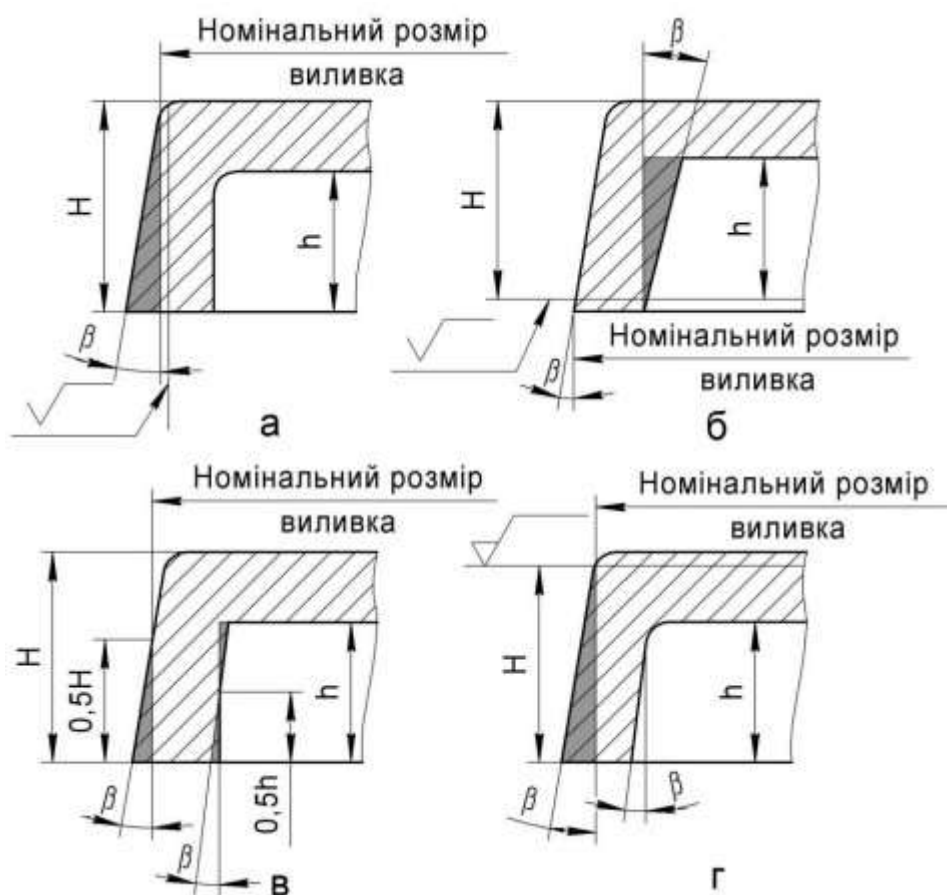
Формувальні ухили для необроблених поверхонь
